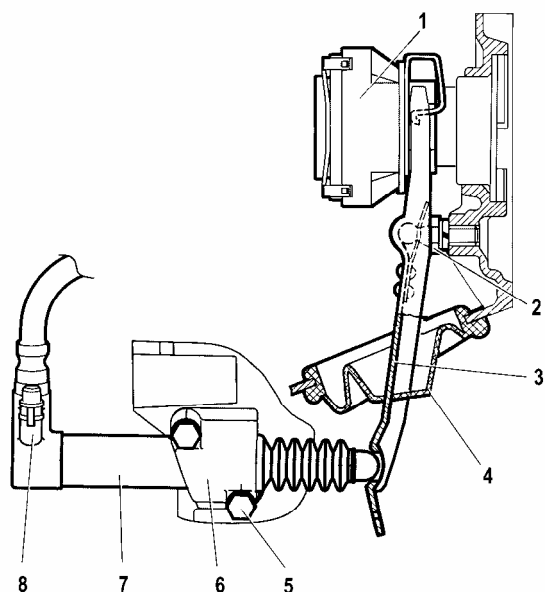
Рабочий цилиндр и вилка выключения сцепления:
